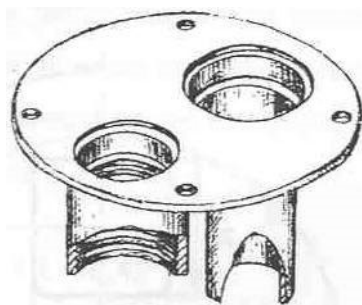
Внешний вид приспособления ШВЕА.301314.025
